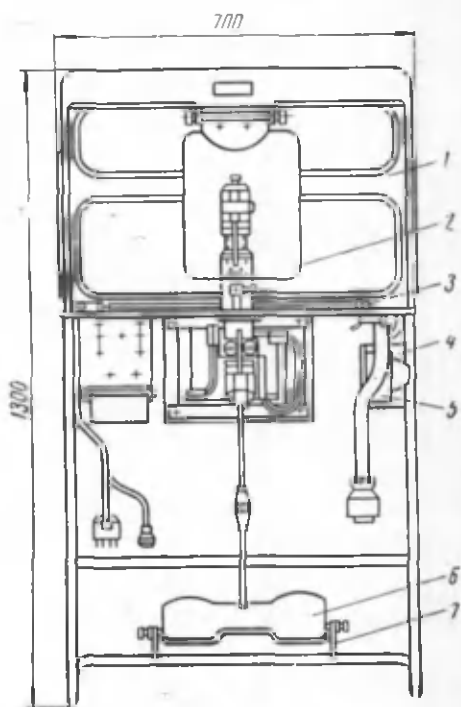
Конструкция монтажно-сварочного стола:
